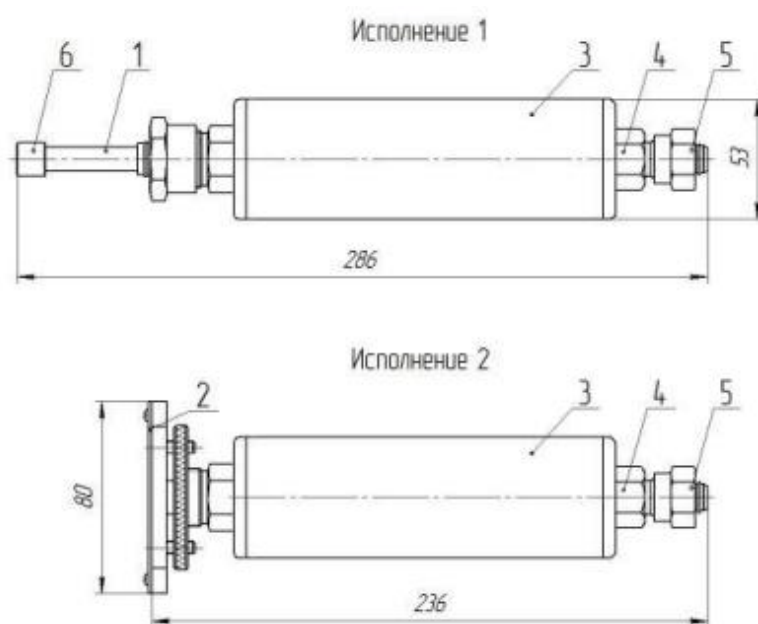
Конструкция капиллярной контрольной течи, где 1 – патрубок для присоединения к испытываемой системе или барокамере; 2 – линейка для настройки щупа; 3 – корпус; 4 – заправочный клапан; 5, 6 – заглушка.
